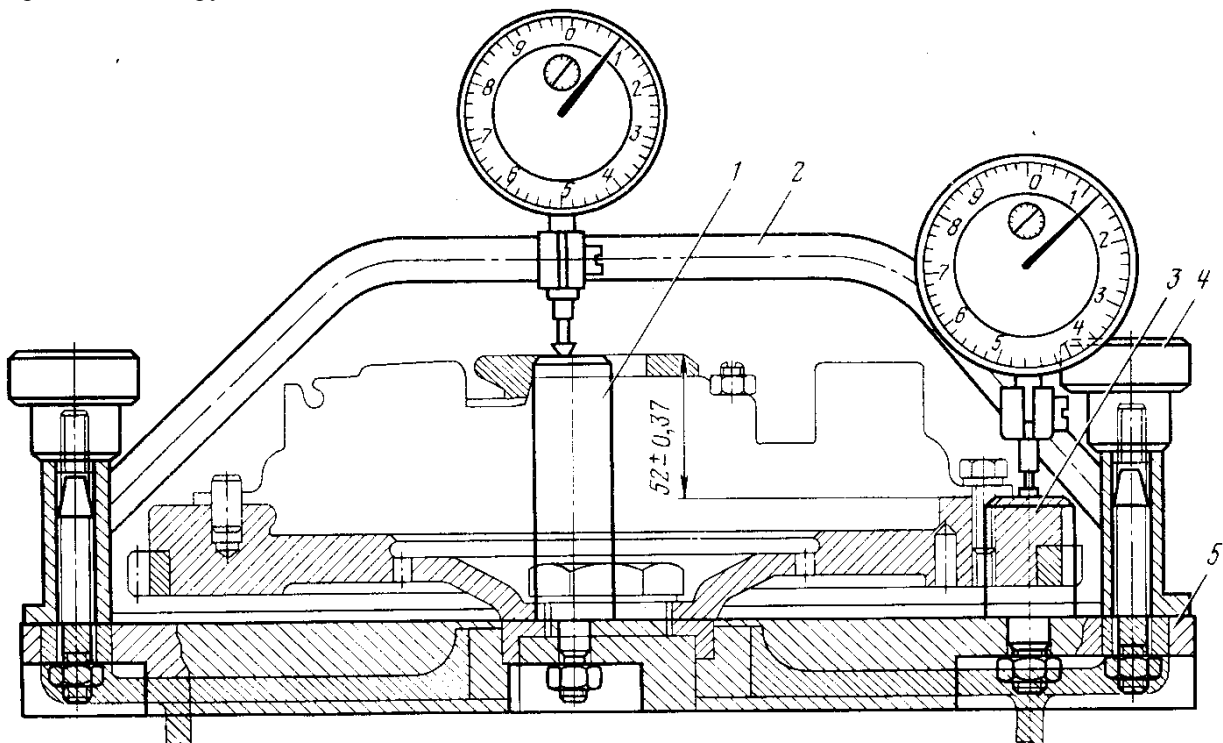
Приспособление для проверки биения торца маховика и для регулировки положения пяты рычагов сцепления:
